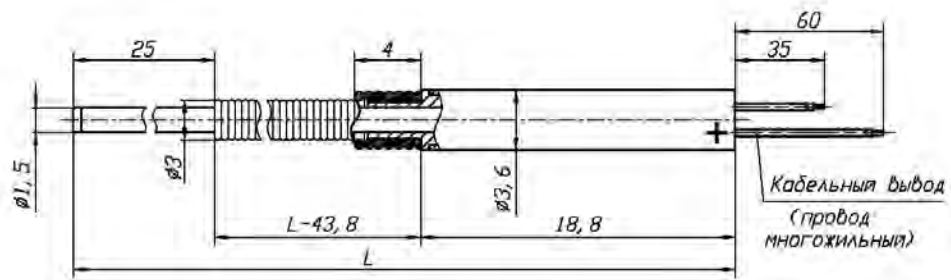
ж – Габаритный чертеж ТТ моделей ТХА 001.06Сп-Ехі, ТХА 001.06Сп-Ехп с двумя установочными узлами
